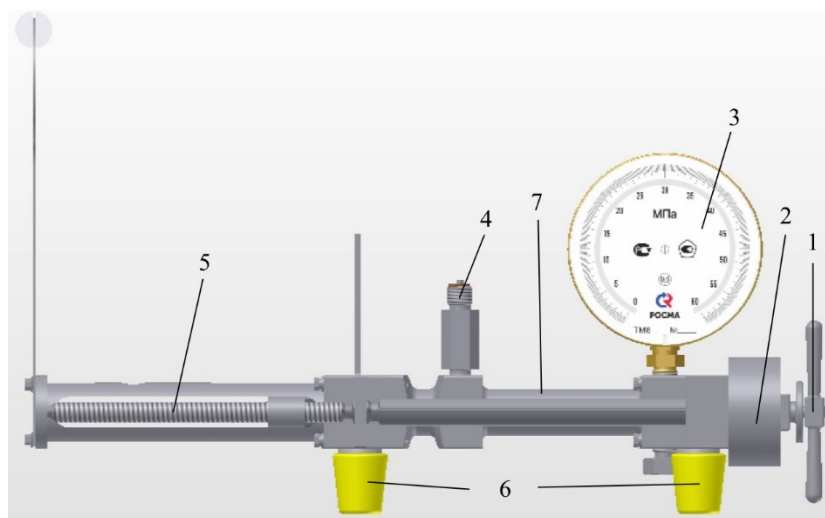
Модель камеры давления. 1- ручка установки давления, 2 – редуктор, 3 – манометр, 4 – втулка подключения измерительной ячейки, 5 – винтовая передача поршня, 6 – ножки, 7 – цилиндр с гидравлической жидкостью и поршнем.
